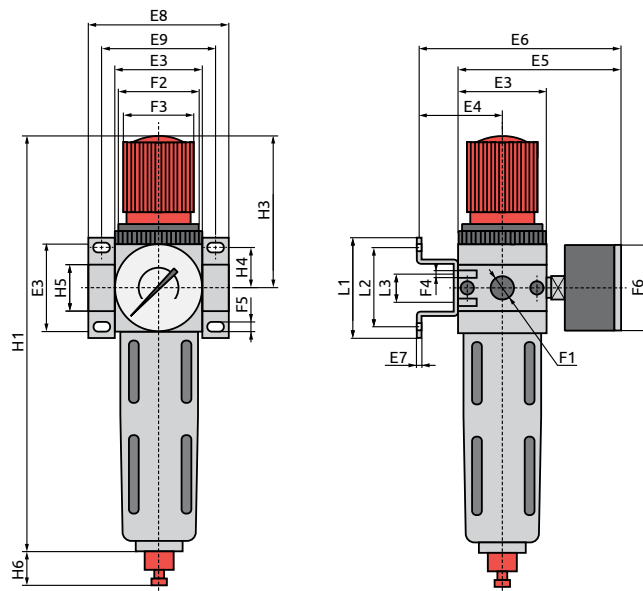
Габаритные размеры блоков подготовки сжатого воздуха ATU-FR
